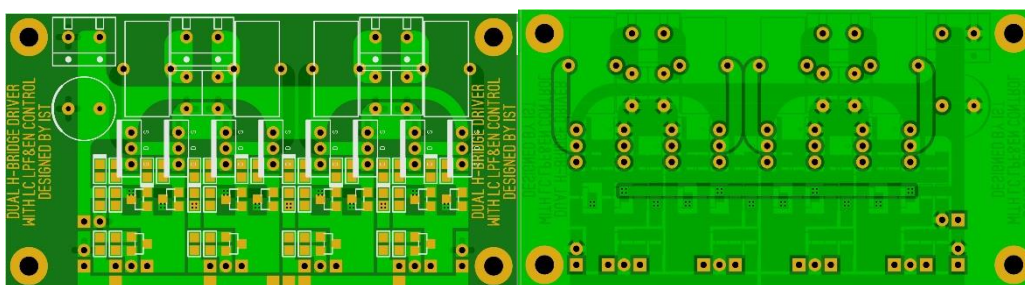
双路 H 桥电机驱动电路 PCB 设计图正面与反面
